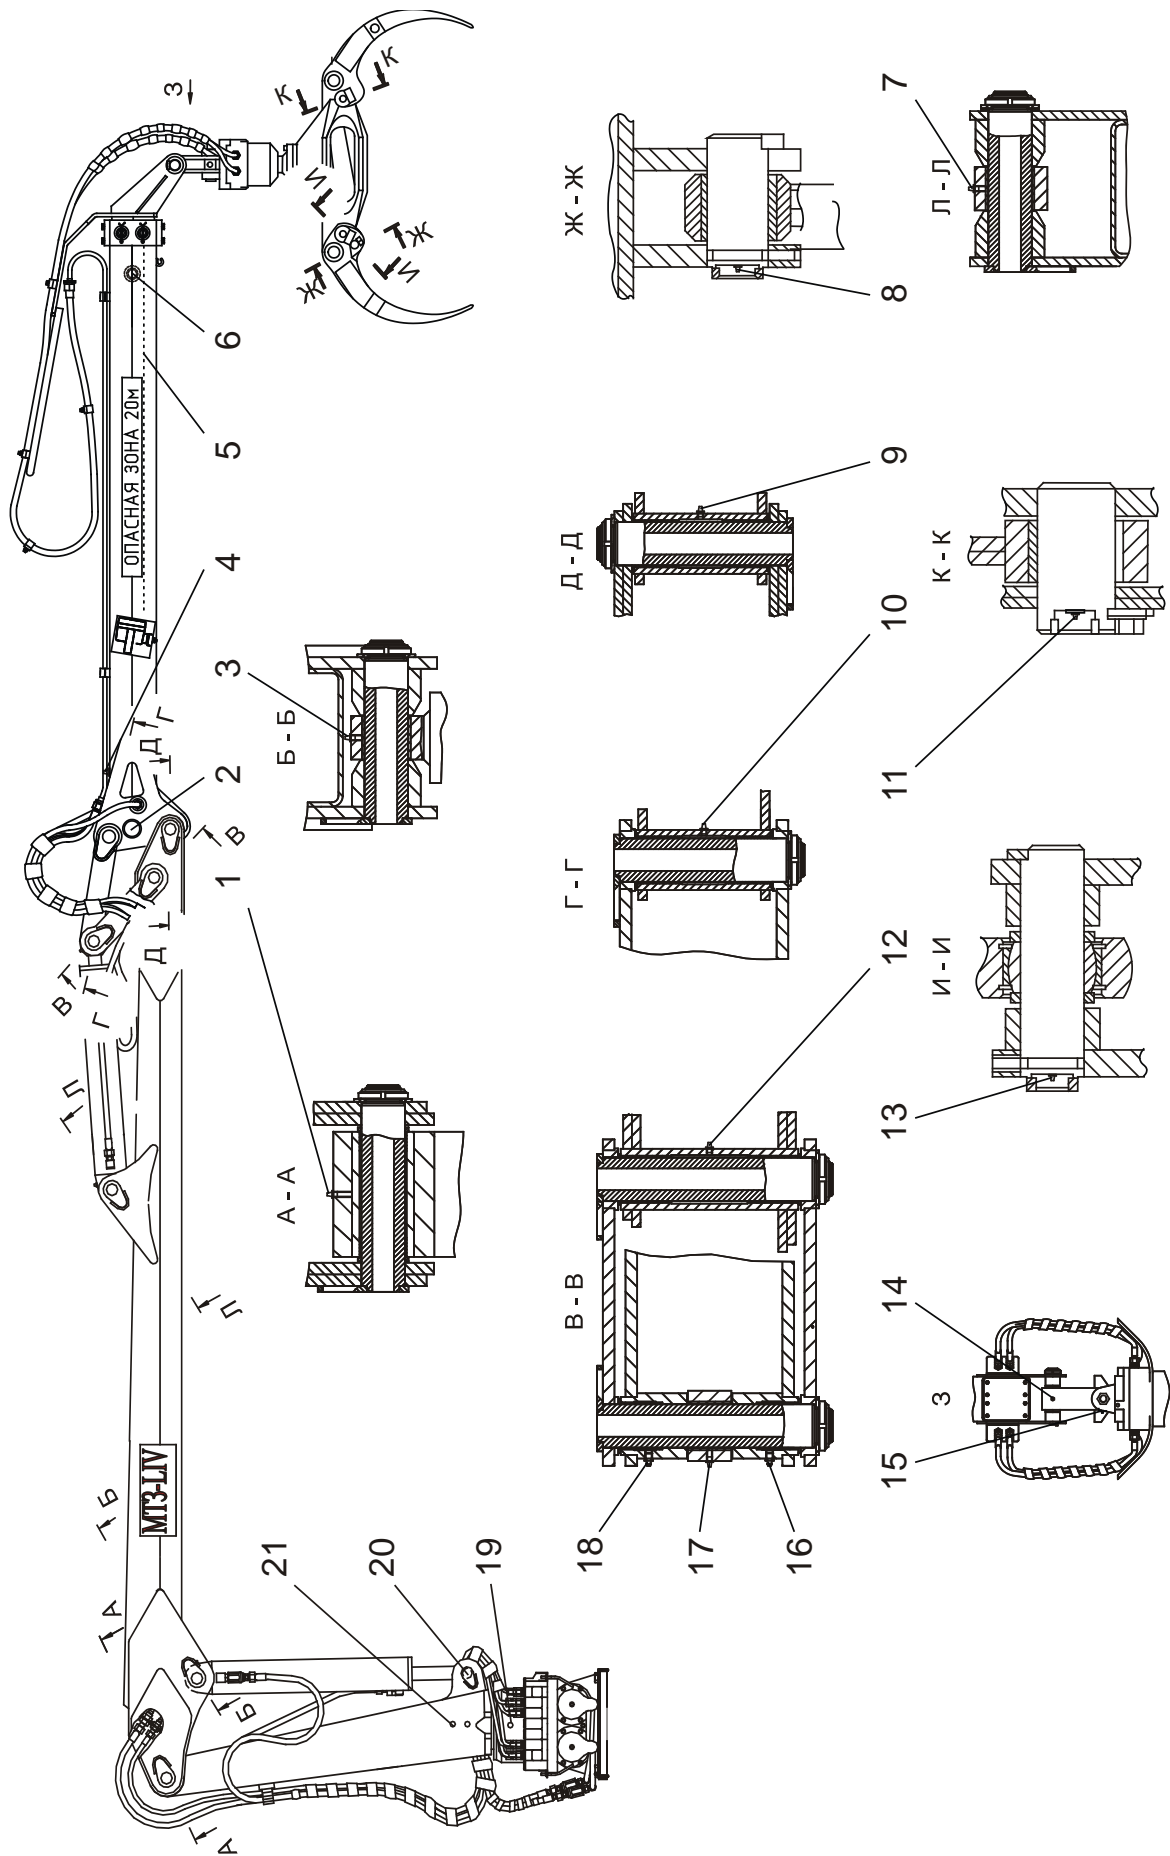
Схема смазки (заправки) гидроманипулятора
